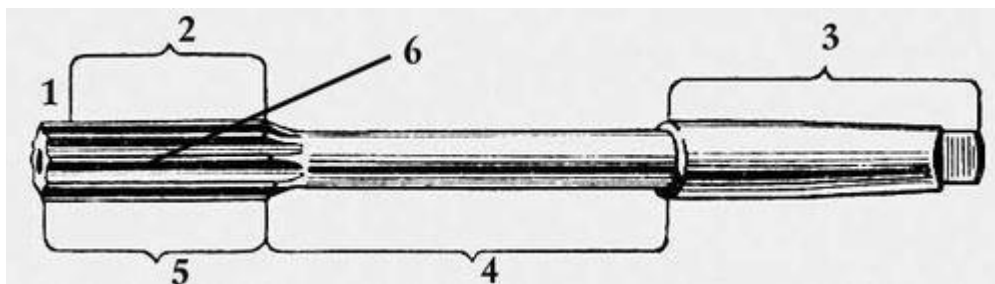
схема развёртки 1 — режущая часть; 2 — калибрующая часть; 3 — хвостовик; 4 — шейка; 5 — рабочая часть; 6 — зуб.
